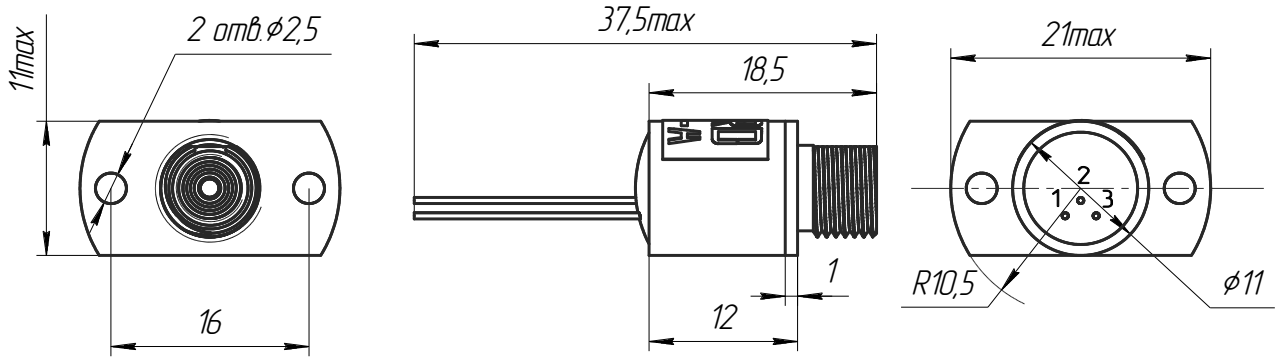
Габаритные размеры модулей OMTD-03/OMRD-03.
